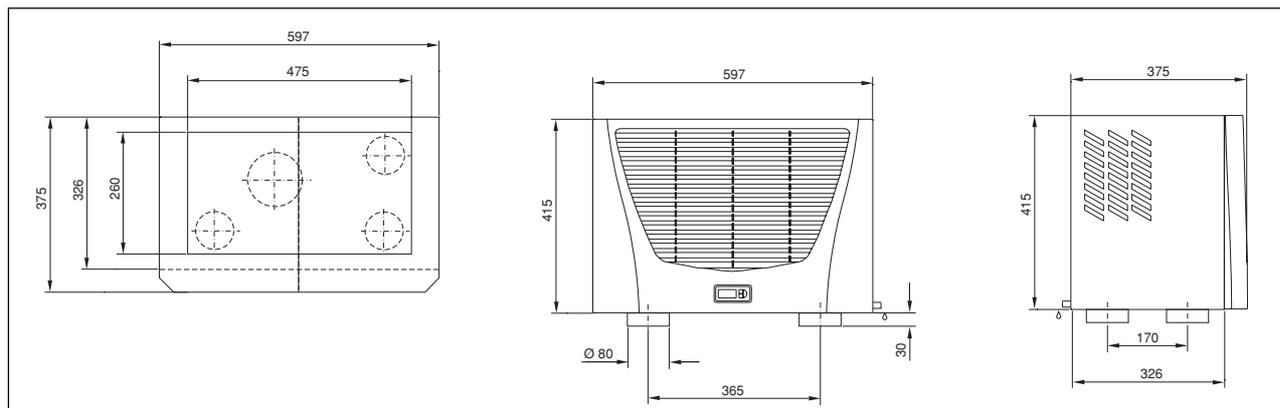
SK 3359.xxx, SK 3382.xxx montaggio sul tetto
